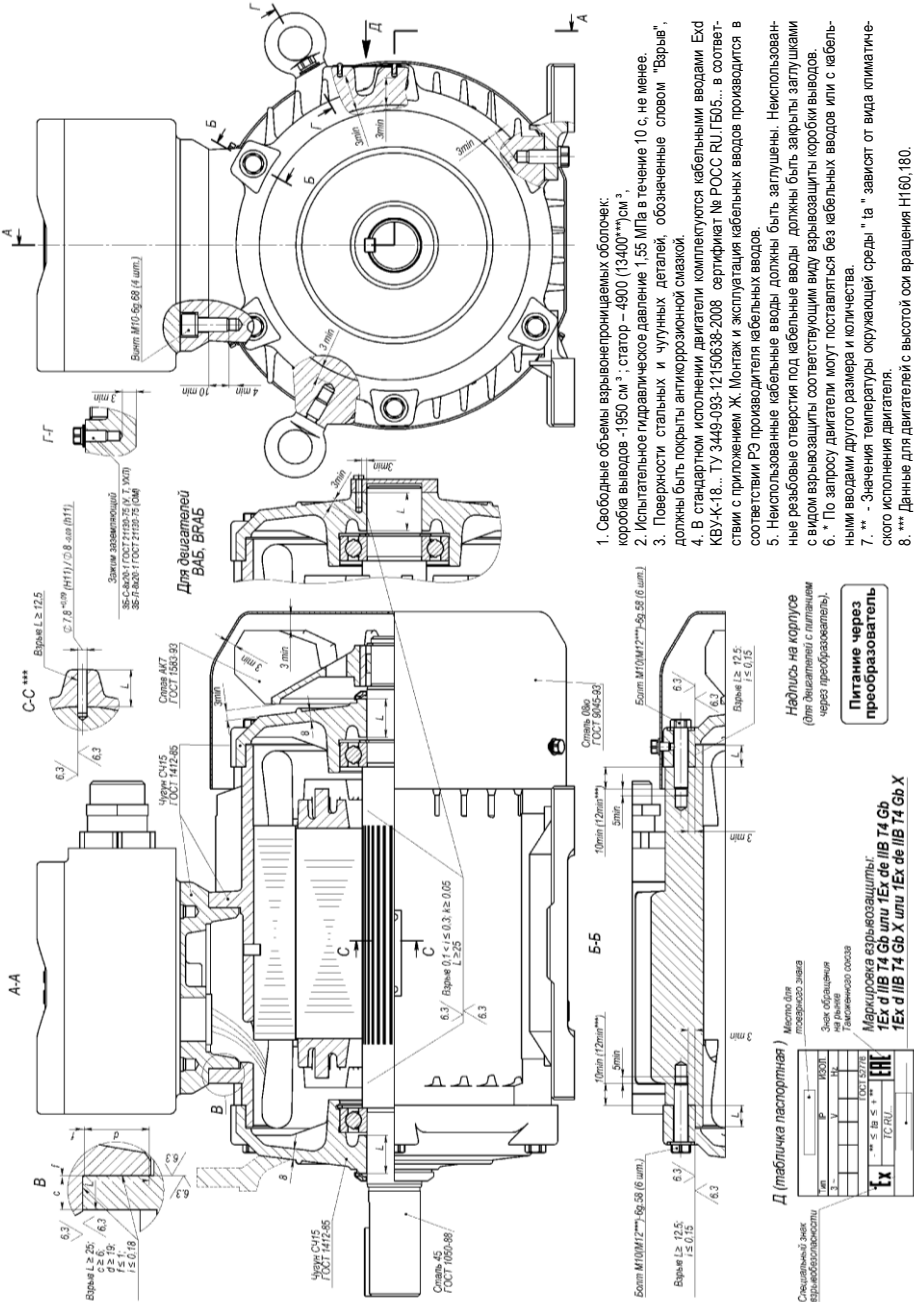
Чертеж средств взрывозащиты двигателя ВА
